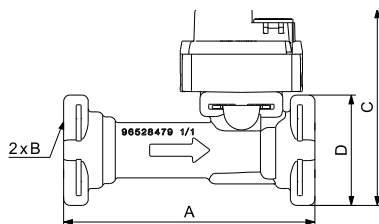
Abmessungen des Sensors VFS 1-20 l/min (ohne Adapter)
